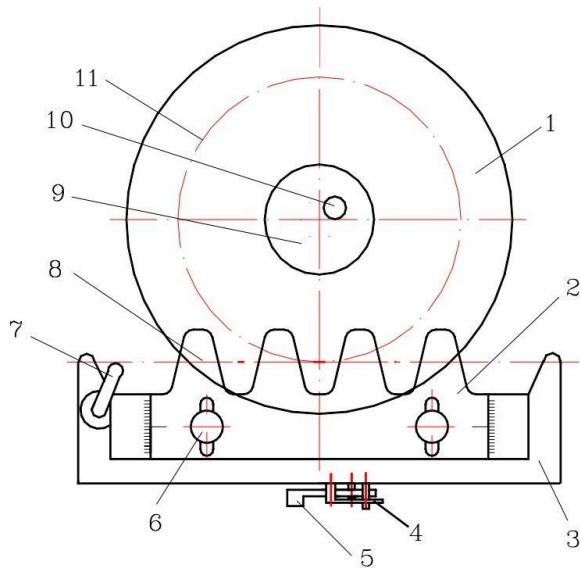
Схема лабораторной установки ТММ 42 для профилирования зубьев зубчатого колеса:
